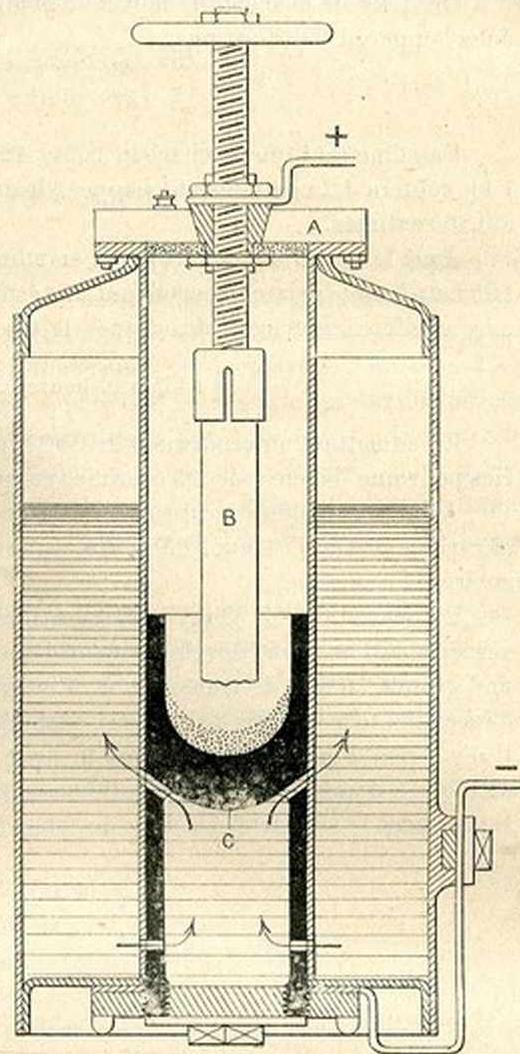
Coupe de la chaudière électrique Ougrimoff.
